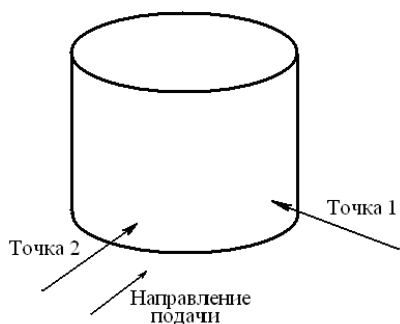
Расположение контрольных точек измерения вибрации на шпинделе вертикально-фрезерного станка
